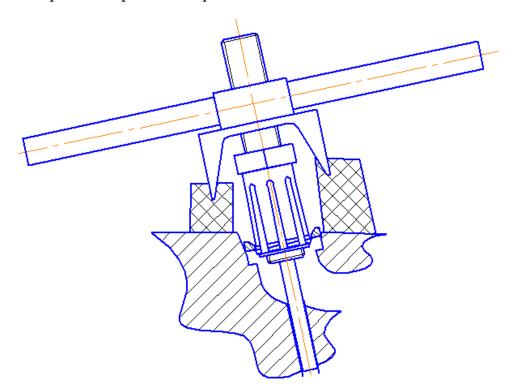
Выпрессовка кольца клапанного седла
